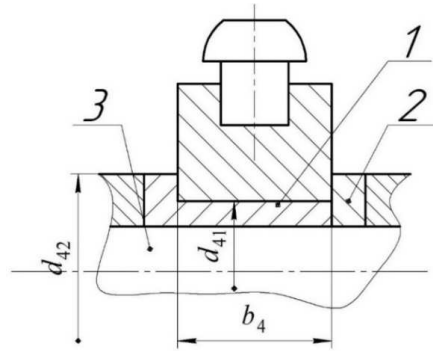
Конструкция подшипника скольжения для составного ролика
